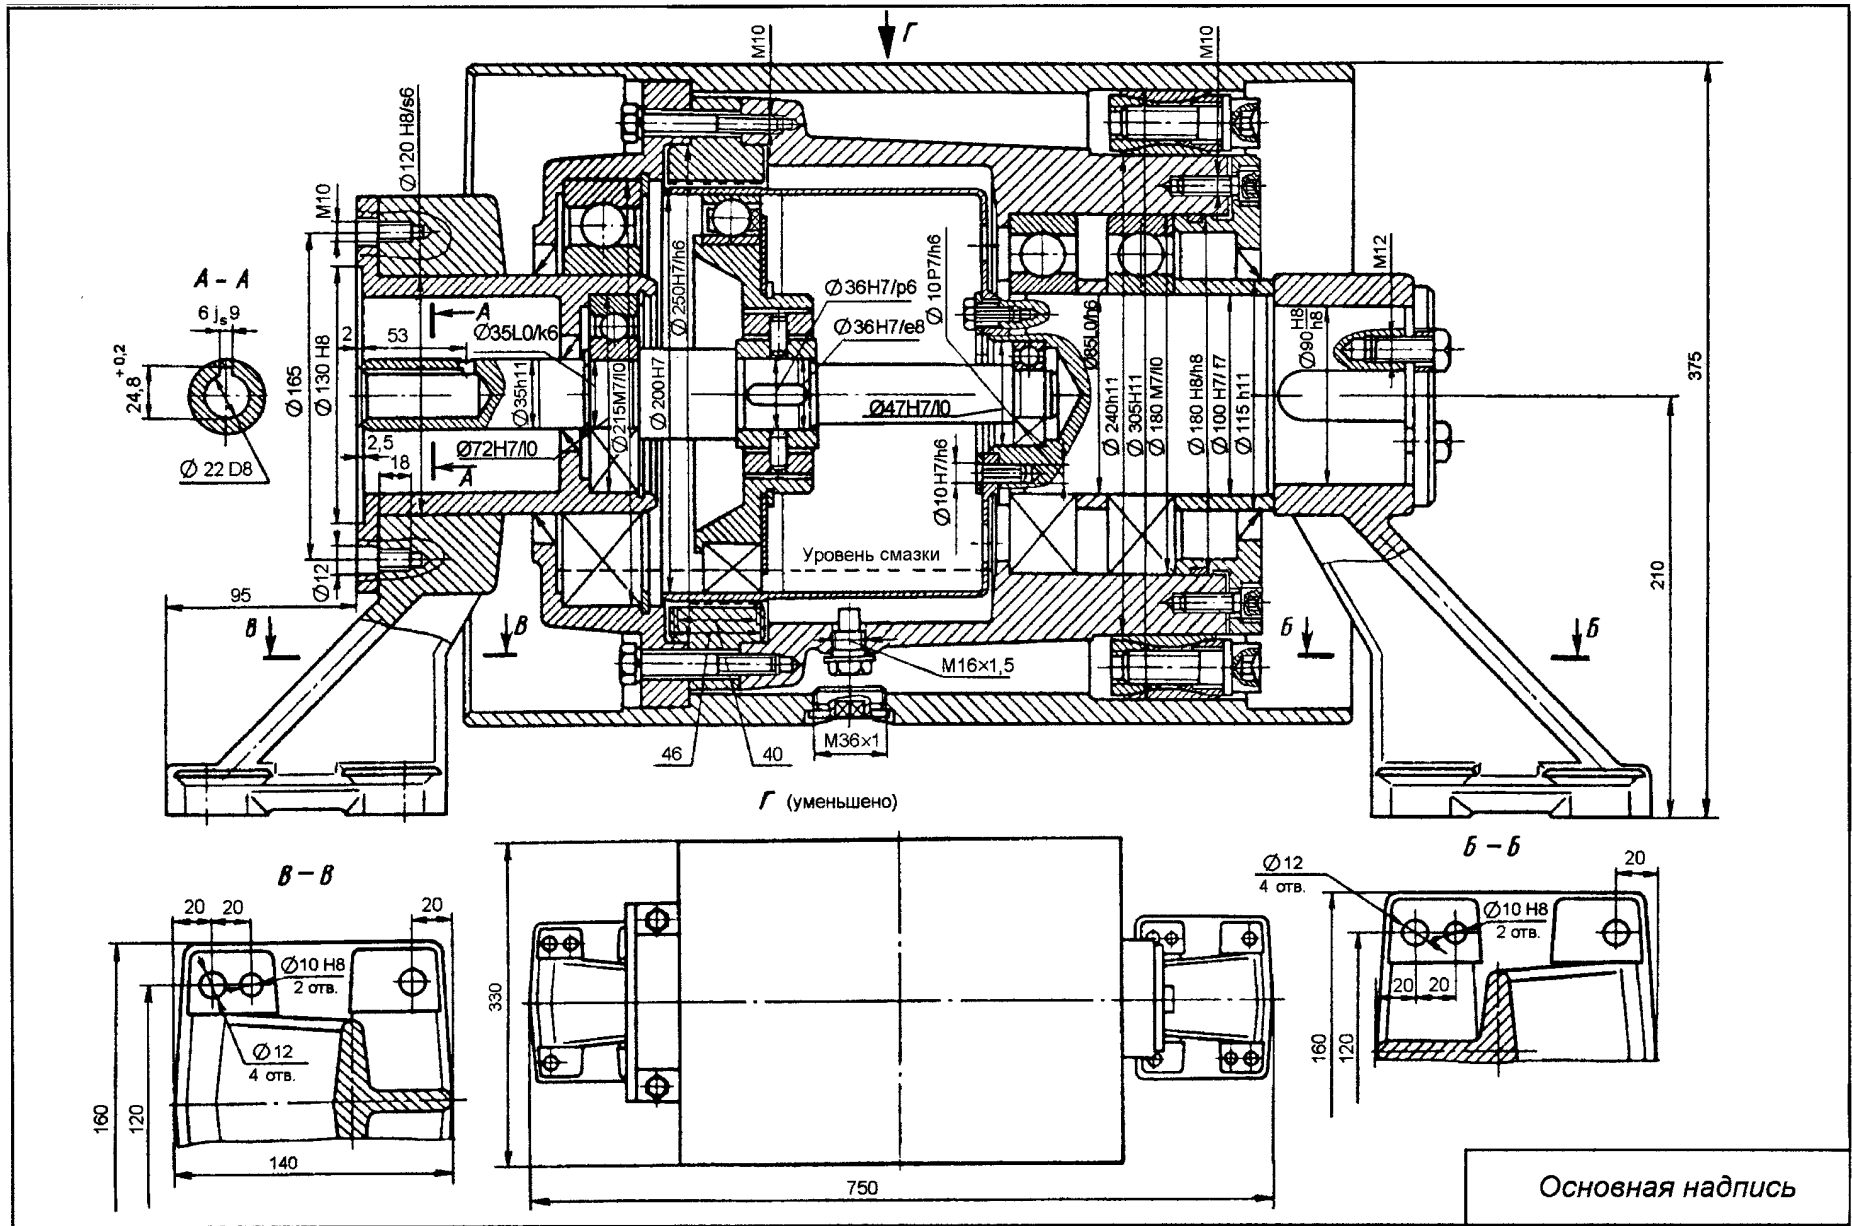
Барабан-редуктор транспортера с волновой передачей (развертка)
